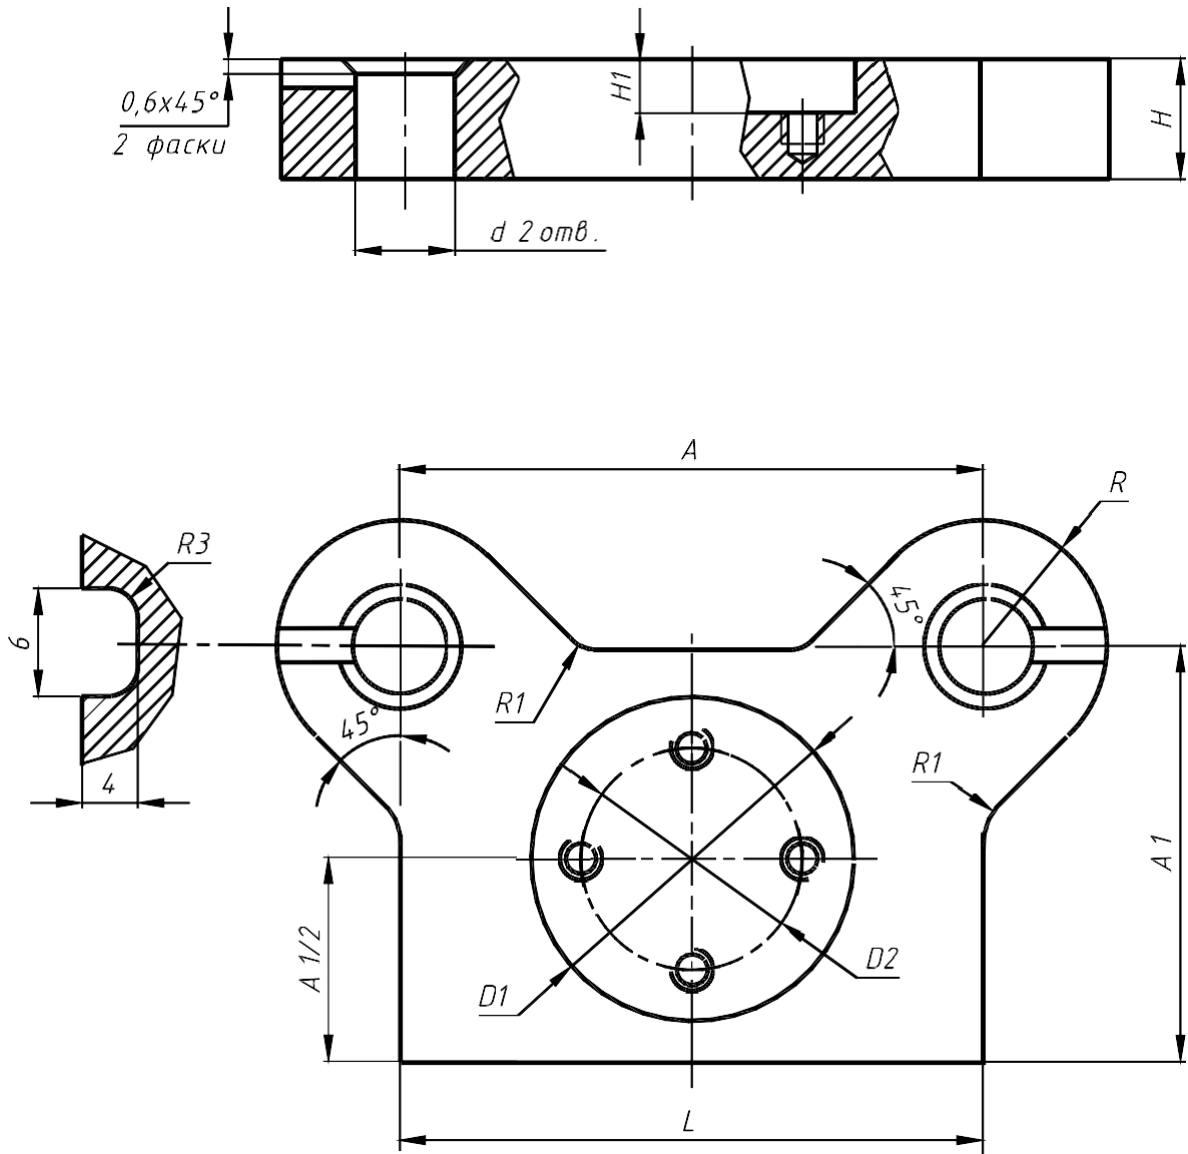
Чертеж с параметрами верхней плиты блока штампа
